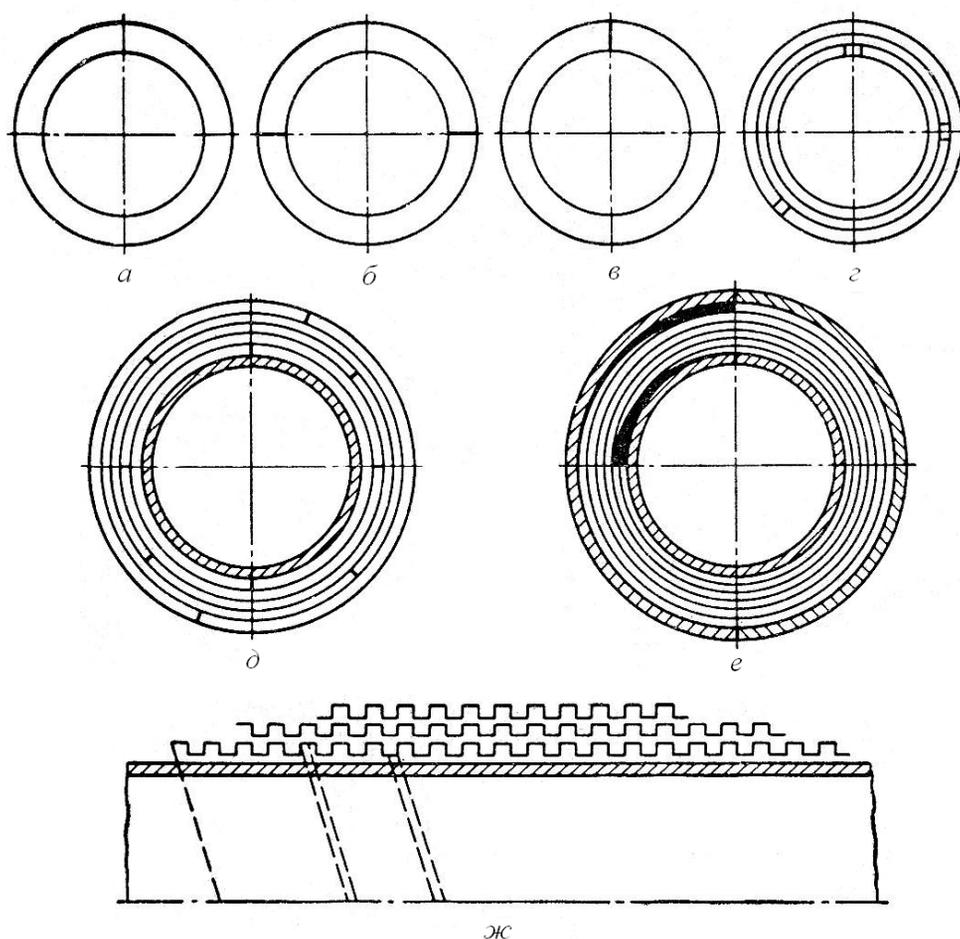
Конструкции корпусов аппаратов высокого давления
